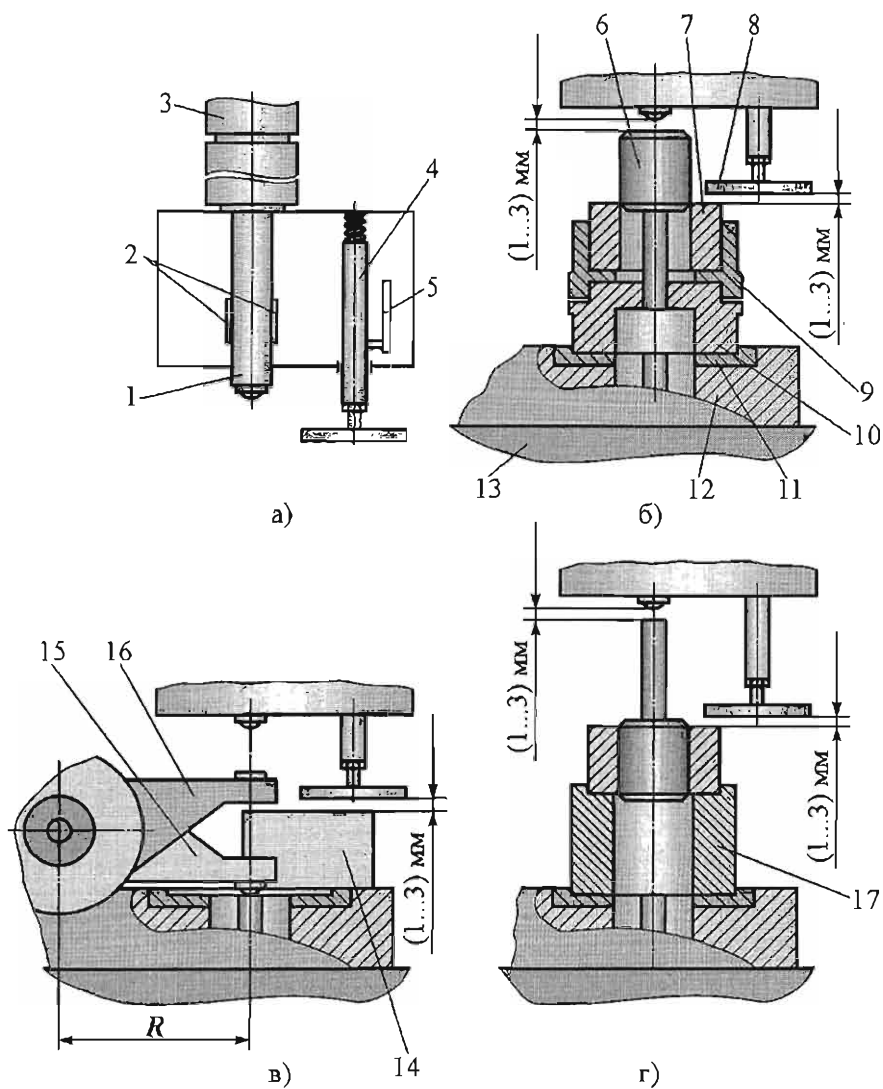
Приспособление ДМ-26А для исследования соединений с натягом:
